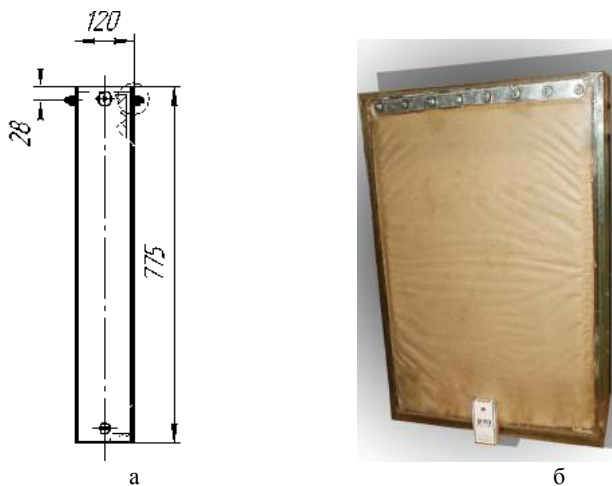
Конденсатор КИМ-120: а – габаритные размеры, б – внешний вид
